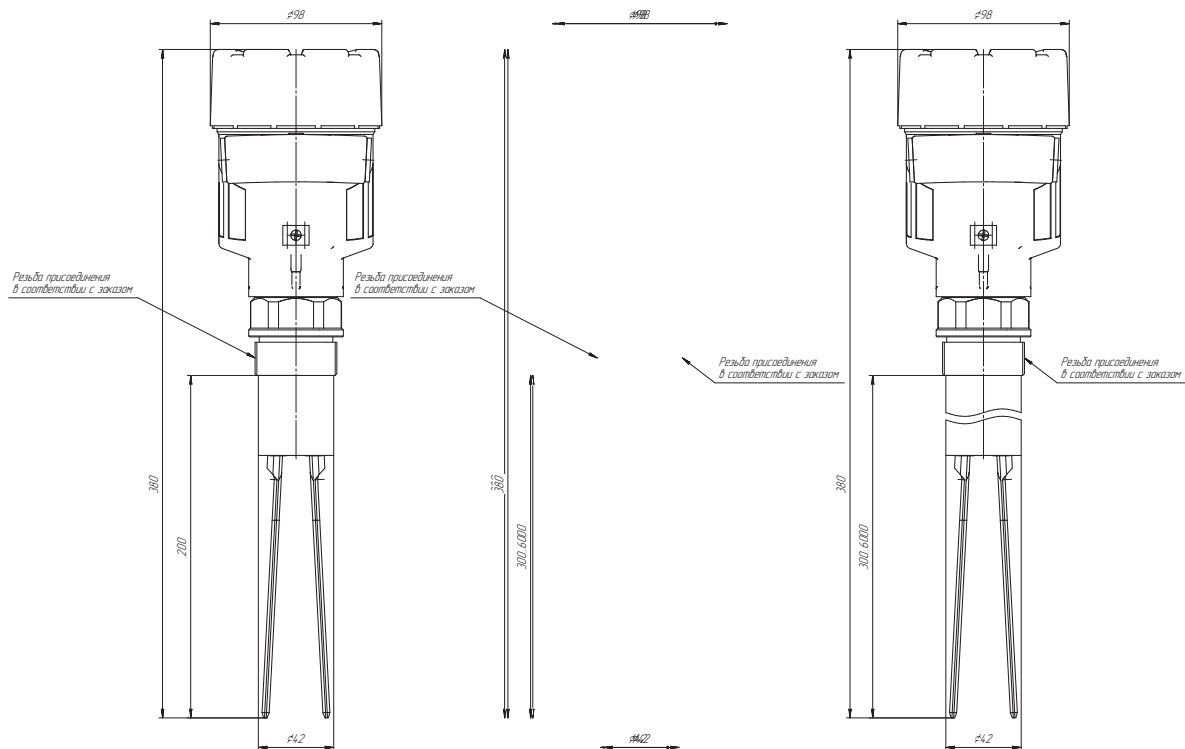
Габаритные размеры резьбового сигнализатора, стандартного (слева) и удлиненного (справа) исполнений, для контроля сыпучих сред
